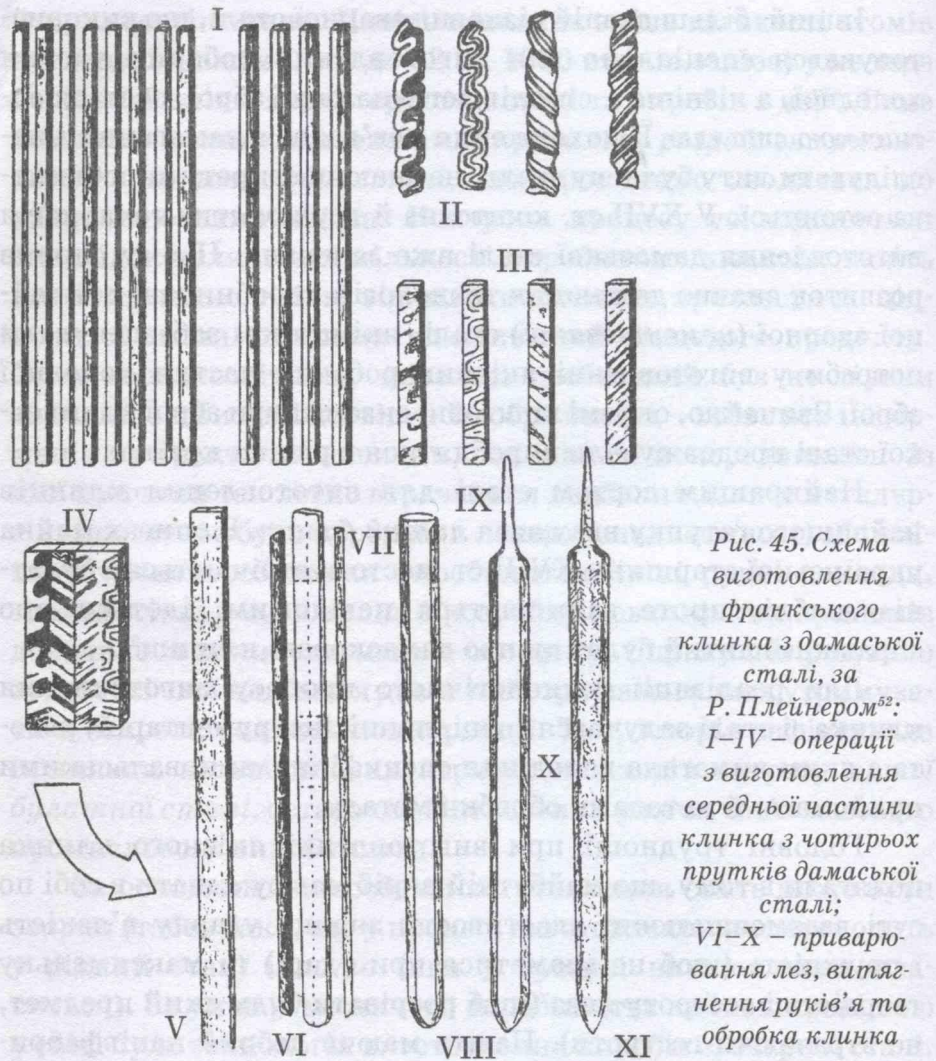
Схема виготовлення франкського клинка з дамаської сталі, за Р. Плейнером⁵²: I–IV – операції з виготовлення середньої частини клинка з чотирьох прутків дамаської сталі; VI–X – приварювання лез, витягнення руків'я та обробка клинка
